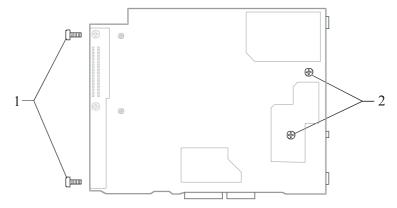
1 2 Schrauben Rückseite 2 2 Schrauben Leiterplatte CPU-Chassis
